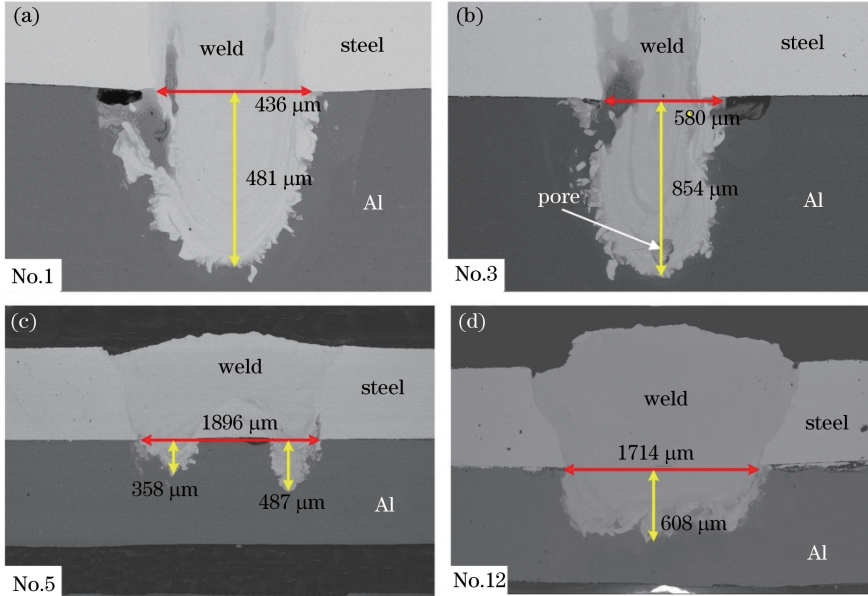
典型焊接工艺参数下获得的焊缝的横截面形貌
